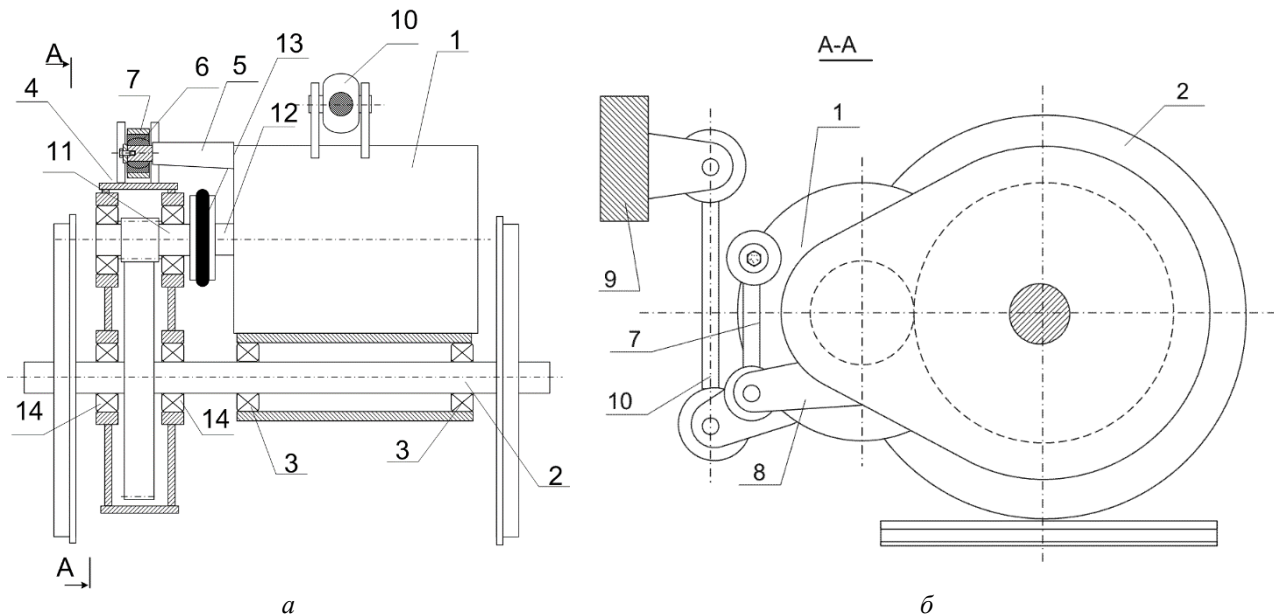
Опорно-осевой привод агрегатной компоновки: *а* – общий вид; *б* – вид со стороны осевого редуктора; 1 – ТЭД; 2 – колесная пара; 3, 14 – подшипники; 4 – осевой редуктор; 5 – кронштейн с пальцем; 6 – сферический шарнир; 7 – подвеска; 8 – кронштейн осевого редуктора; 9 – рама тележки; 10 – подвеска ТЭД; 11 – вал осевого редуктора; 12 – вал ТЭД; 13 – упругокомпенсационная муфта
